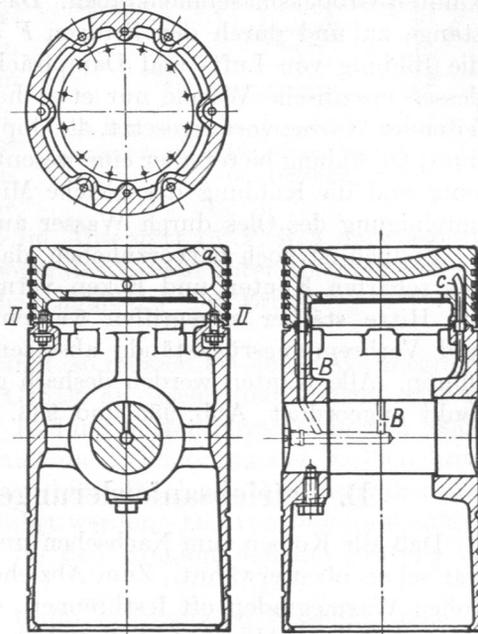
Gasmaschinenkolben mit auswechselbarem, gekühltem Kopf.
